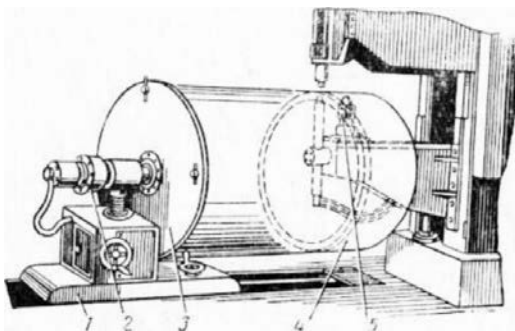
Приспособление для точечной сварки обечайек с механизированным поворотом изделия на шаг сварки: 1 – тележка; 2 – механизм поворота;
